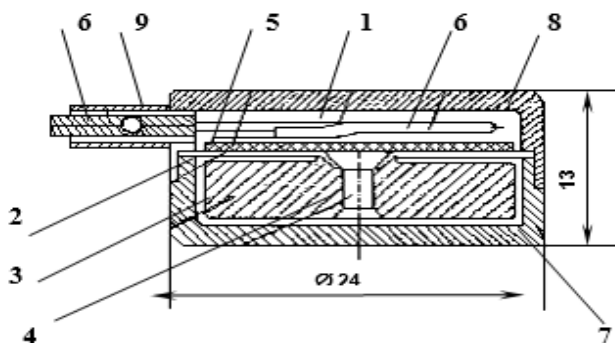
Конструкция акселерометра ПАМТ-1: 1 – пьезопластина (ЦТС-19); 2 – металлическая подложка; 3 – груз; 4 – заклепка; 5 – контактная пластина; 6 – antivибрационный кабель; 7 – корпус; 8 – крышка; 9 – втулка
